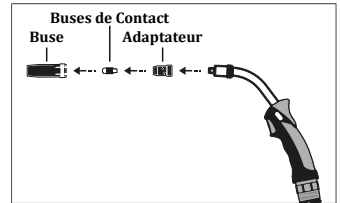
Séparation des Buses et des Buses de Contact de la Torche
